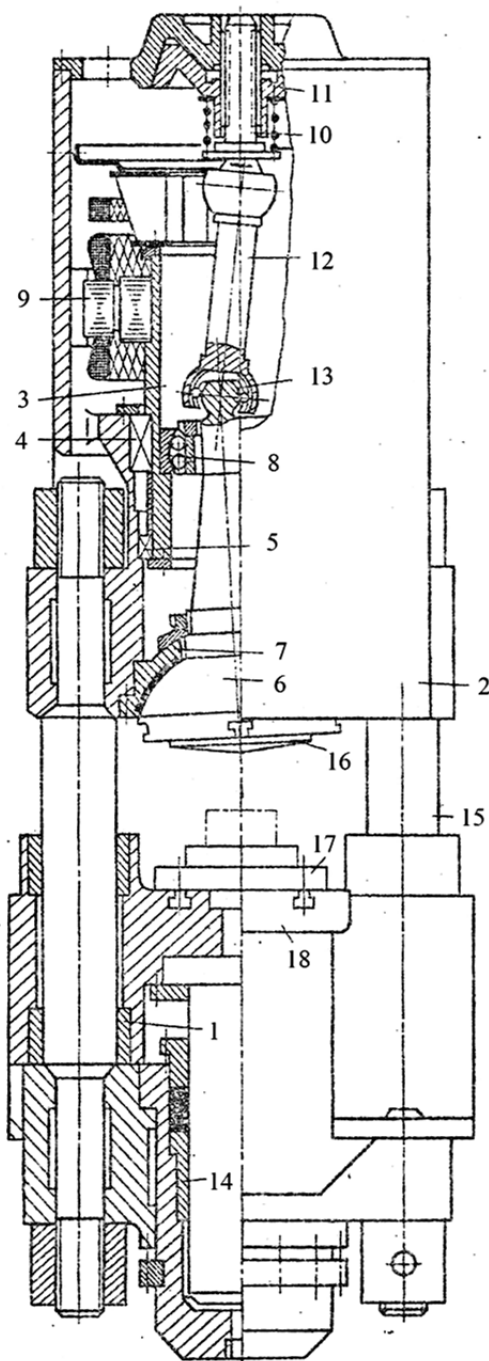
Схема конструкции пресса ПШО-500 (где: 1 - направляющие станины; 2 - подвижная поперечина; 3 - эксцентриковый ротор; 4, 5 - подшипники; 6 - прессователь; 7 - сферический подпятник; 8 - самоустанавливающий подшипник; 9 - ротор 9 электродвигателя; 10 - вал; 11 - тормоз; 12 - промежуточный вал; 13 - синхронные муфты; 14 - механизм осевого перемещения; 15 - тяги; 16, 17 - верхняя и нижняя части штампа; 18 - стол)
